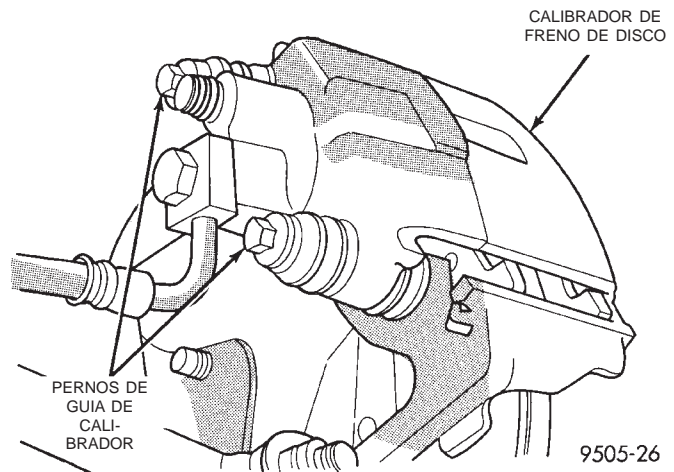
Pernos del pasador guía del conjunto de calibrador
